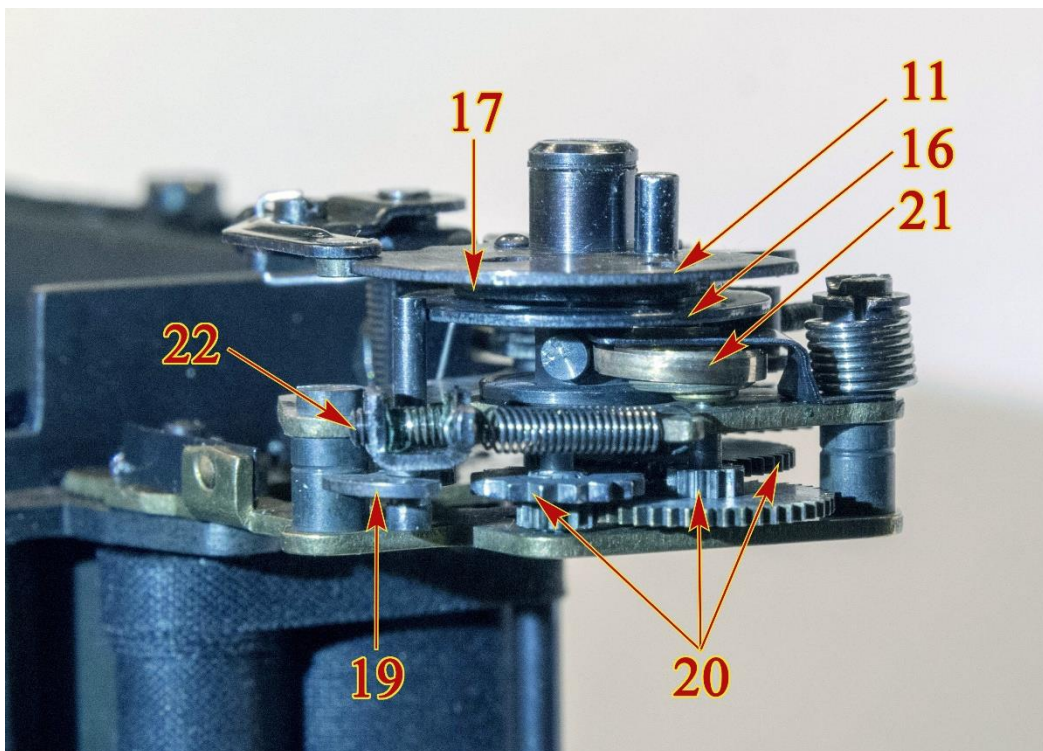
Časovací strojek Pentacon six zabudovaný na nosiči (nastavený na 1/60)
